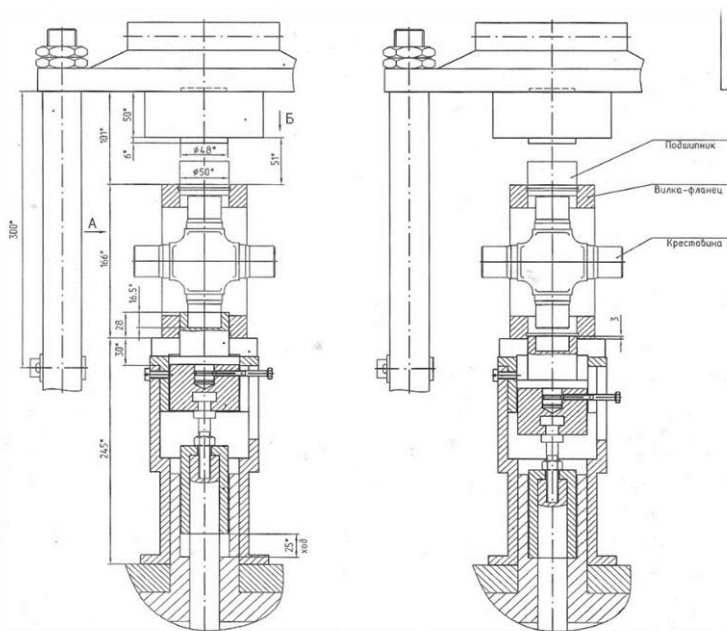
Сборочный чертеж наладки приспособления для сборки карданных валов
